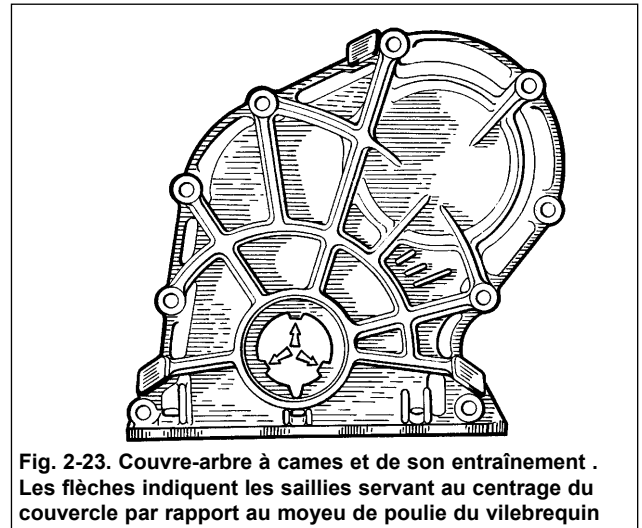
Couvercle-arbre à cames et de son entraînement . Les flèches indiquent les saillies servant au centrage du couvercle par rapport au moyeu de poulie du vilebrequin
